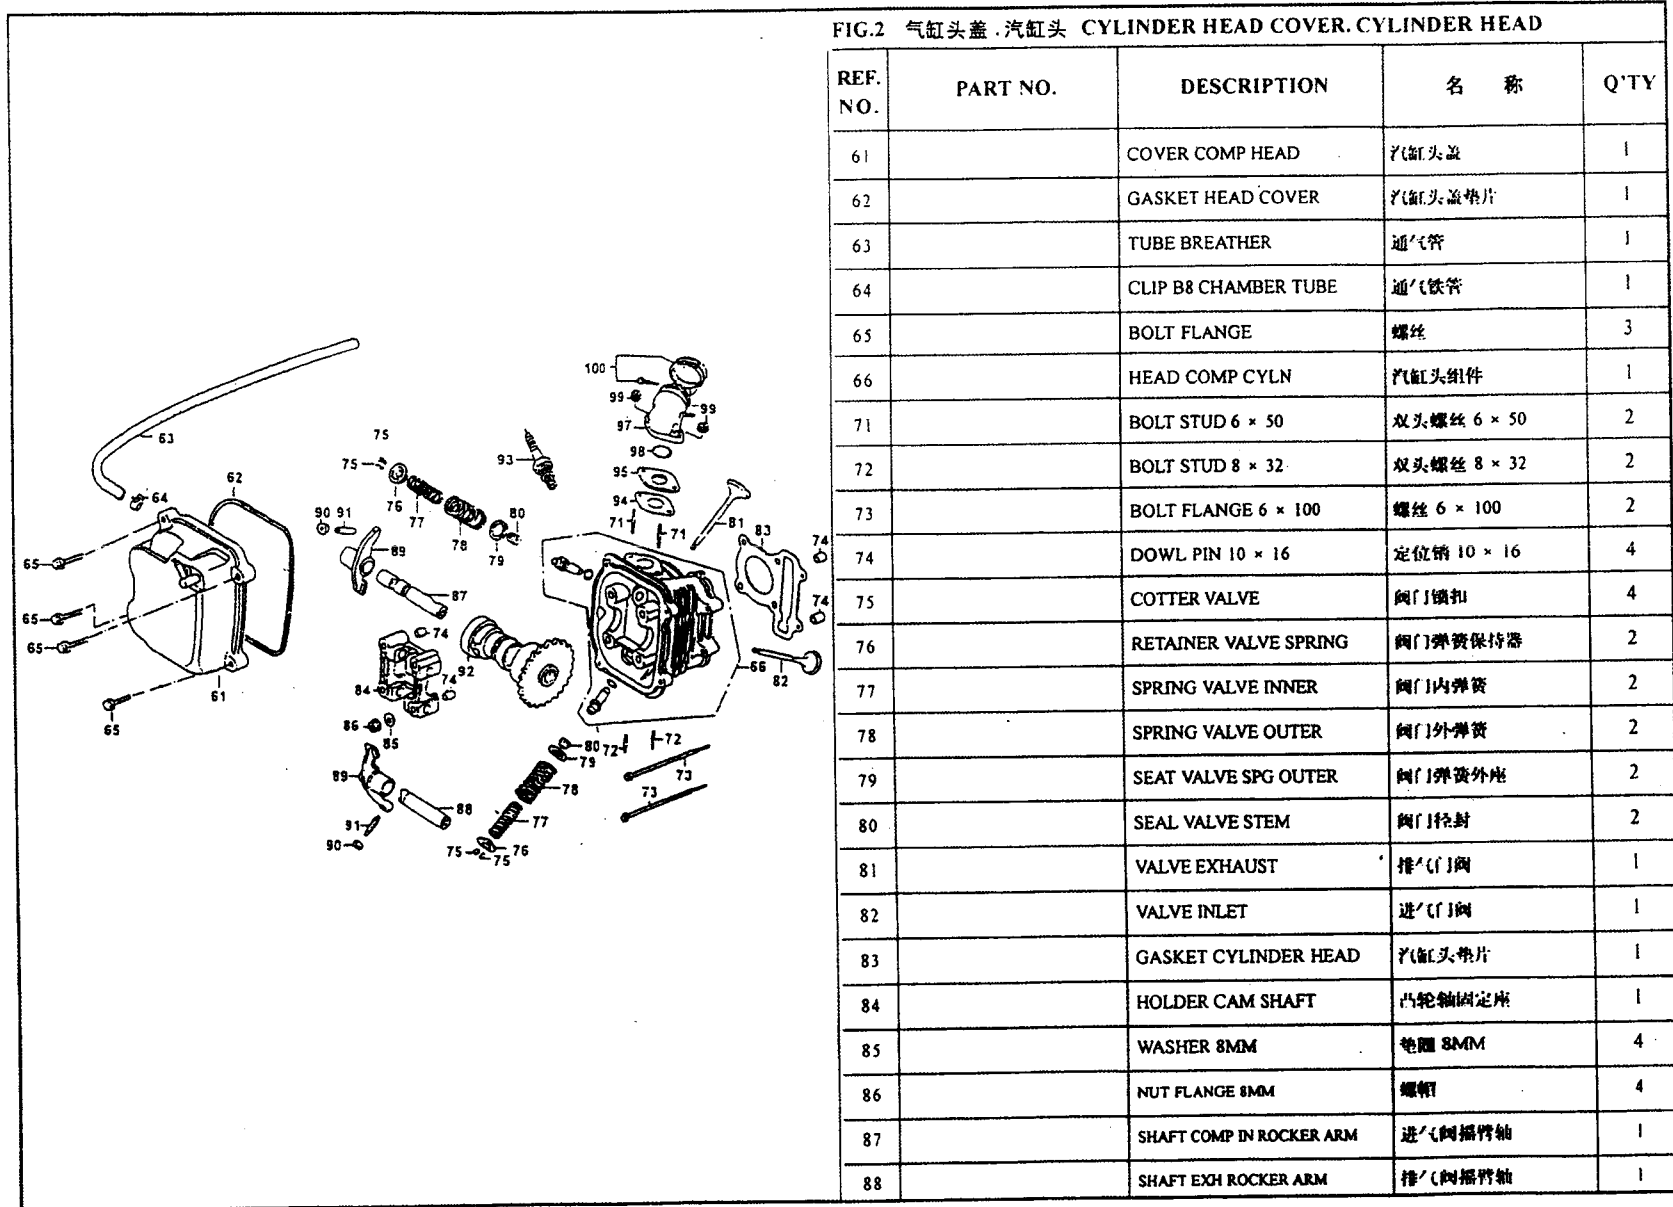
气缸头盖. 汽缸头 CYLINDER HEAD COVER. CYLINDER HEAD
